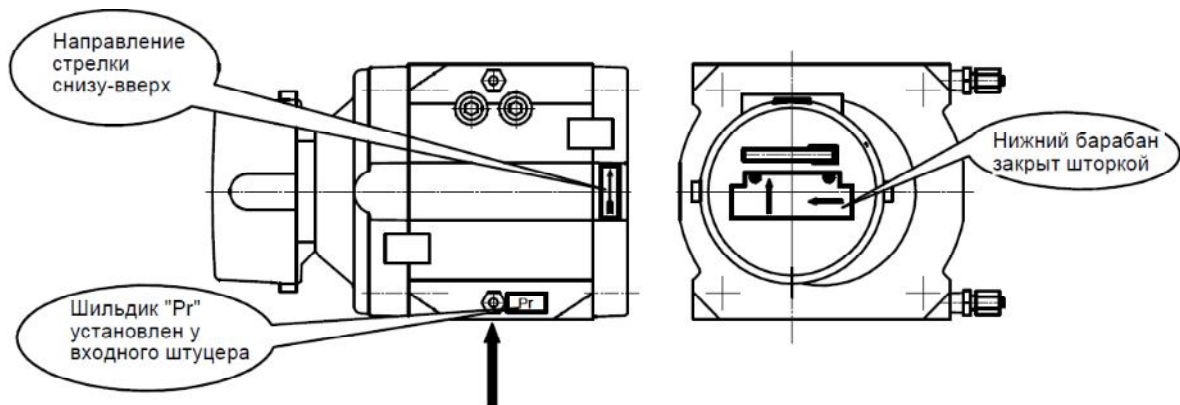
Установка шторки и шильдиков при направлении потока газа снизу-вверх. Счетная голова повернута на 90°
